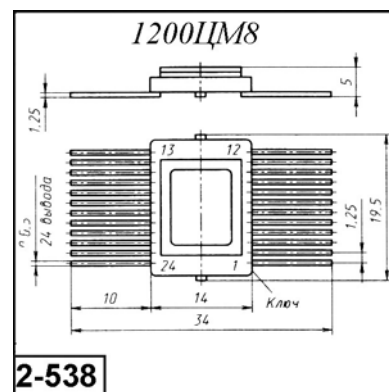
Внешний вид и габаритные размеры 1200ЦМ8
